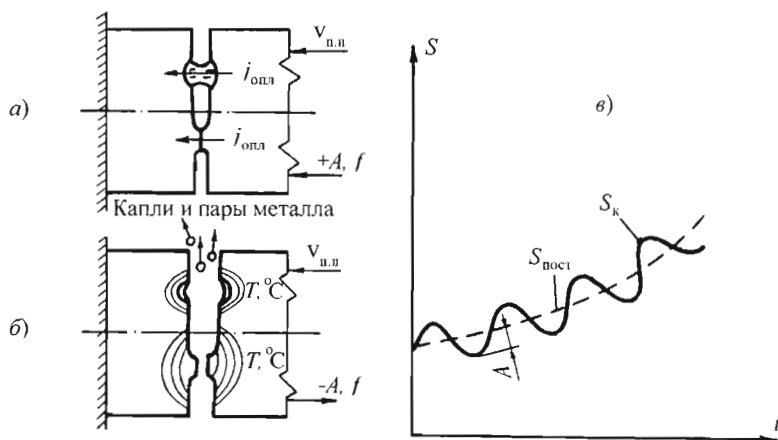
Схема импульсного оплавления при стыковой сварке:
